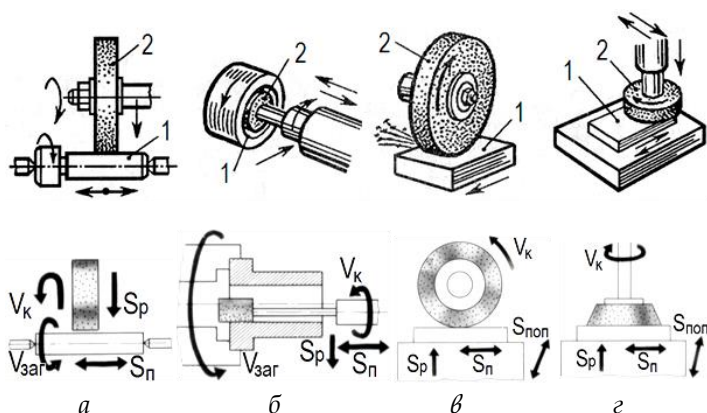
Шлифование круглое наружное (а), круглое внутреннее (б), плоское периферией круга (в) и плоское торцом круга (г): 1 – заготовка; 2 – шлифовальный круг; V_k – скорость главного движения резания; V_{zag} – скорость вращения заготовки; S_n , S_r , S_{nop} – продольная, радиальная и поперечная подача
